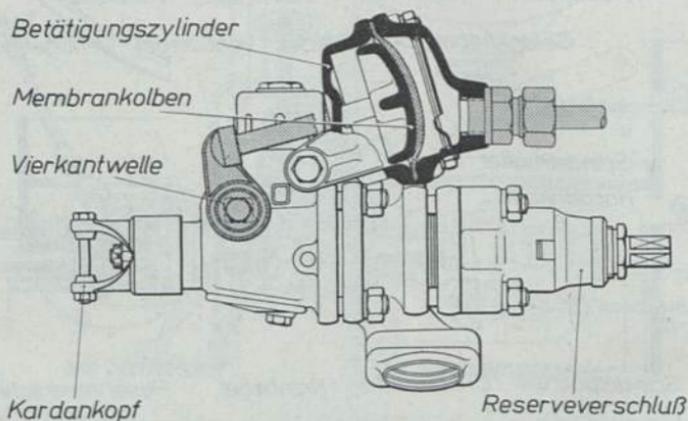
„Gestra“-Betätigungszyylinder mit Membrankolben
